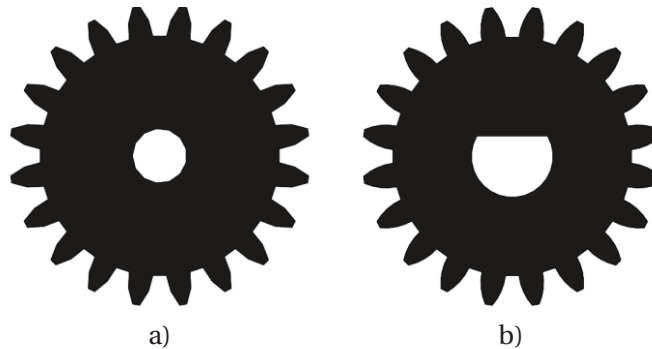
a) Engranajes de 20 dientes con eje circular, b) engranaje de 20 dientes adaptado a eje de *encoder
